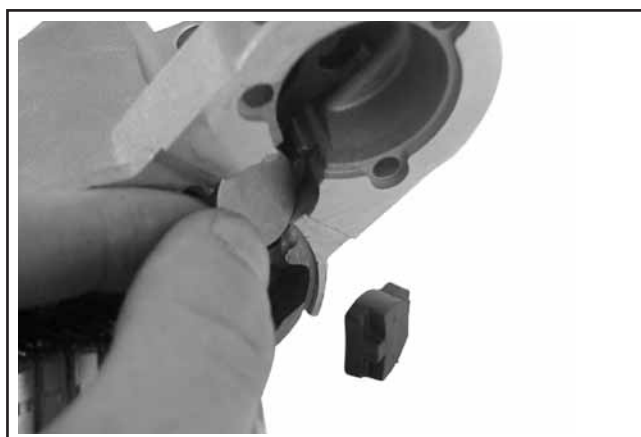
Retrait du coussinet et de la plaque de fond.
